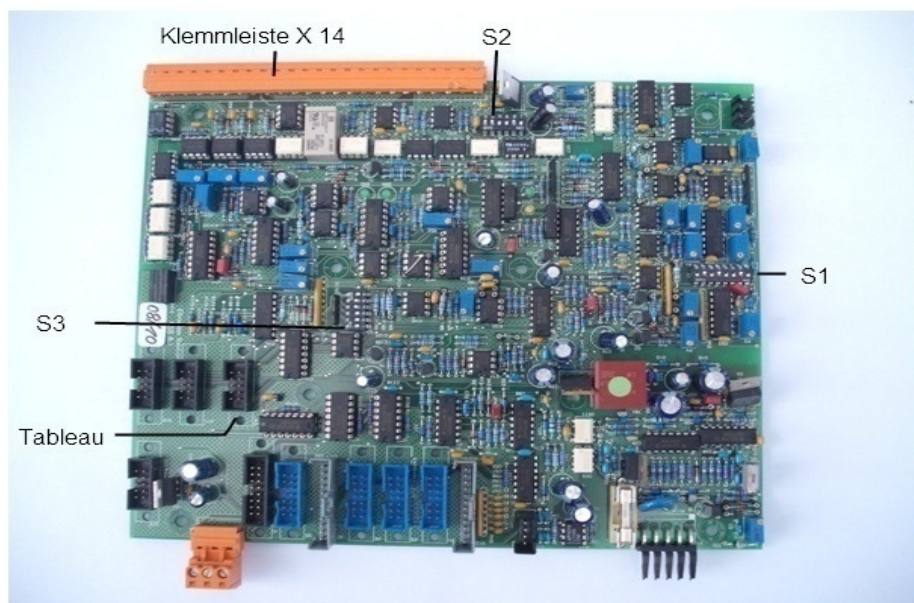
Anschluss- und Bauteile-Lageplan der WSB-Platine
